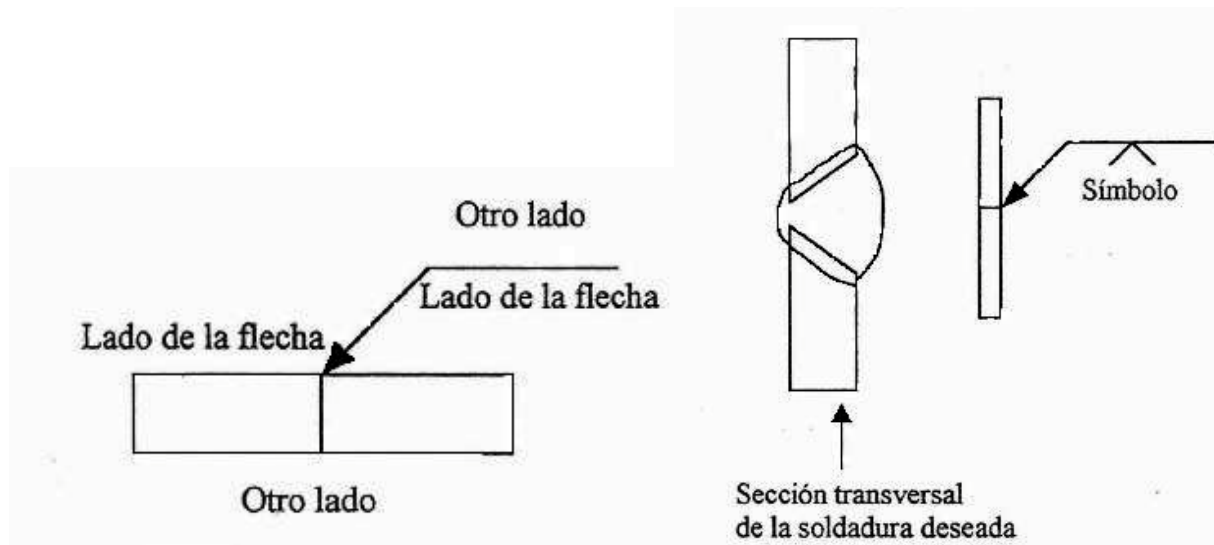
SÍMBOLO PARA UNA SOLDADURA DE RANURA EN "V" AL LADO DE LA FLECHA
